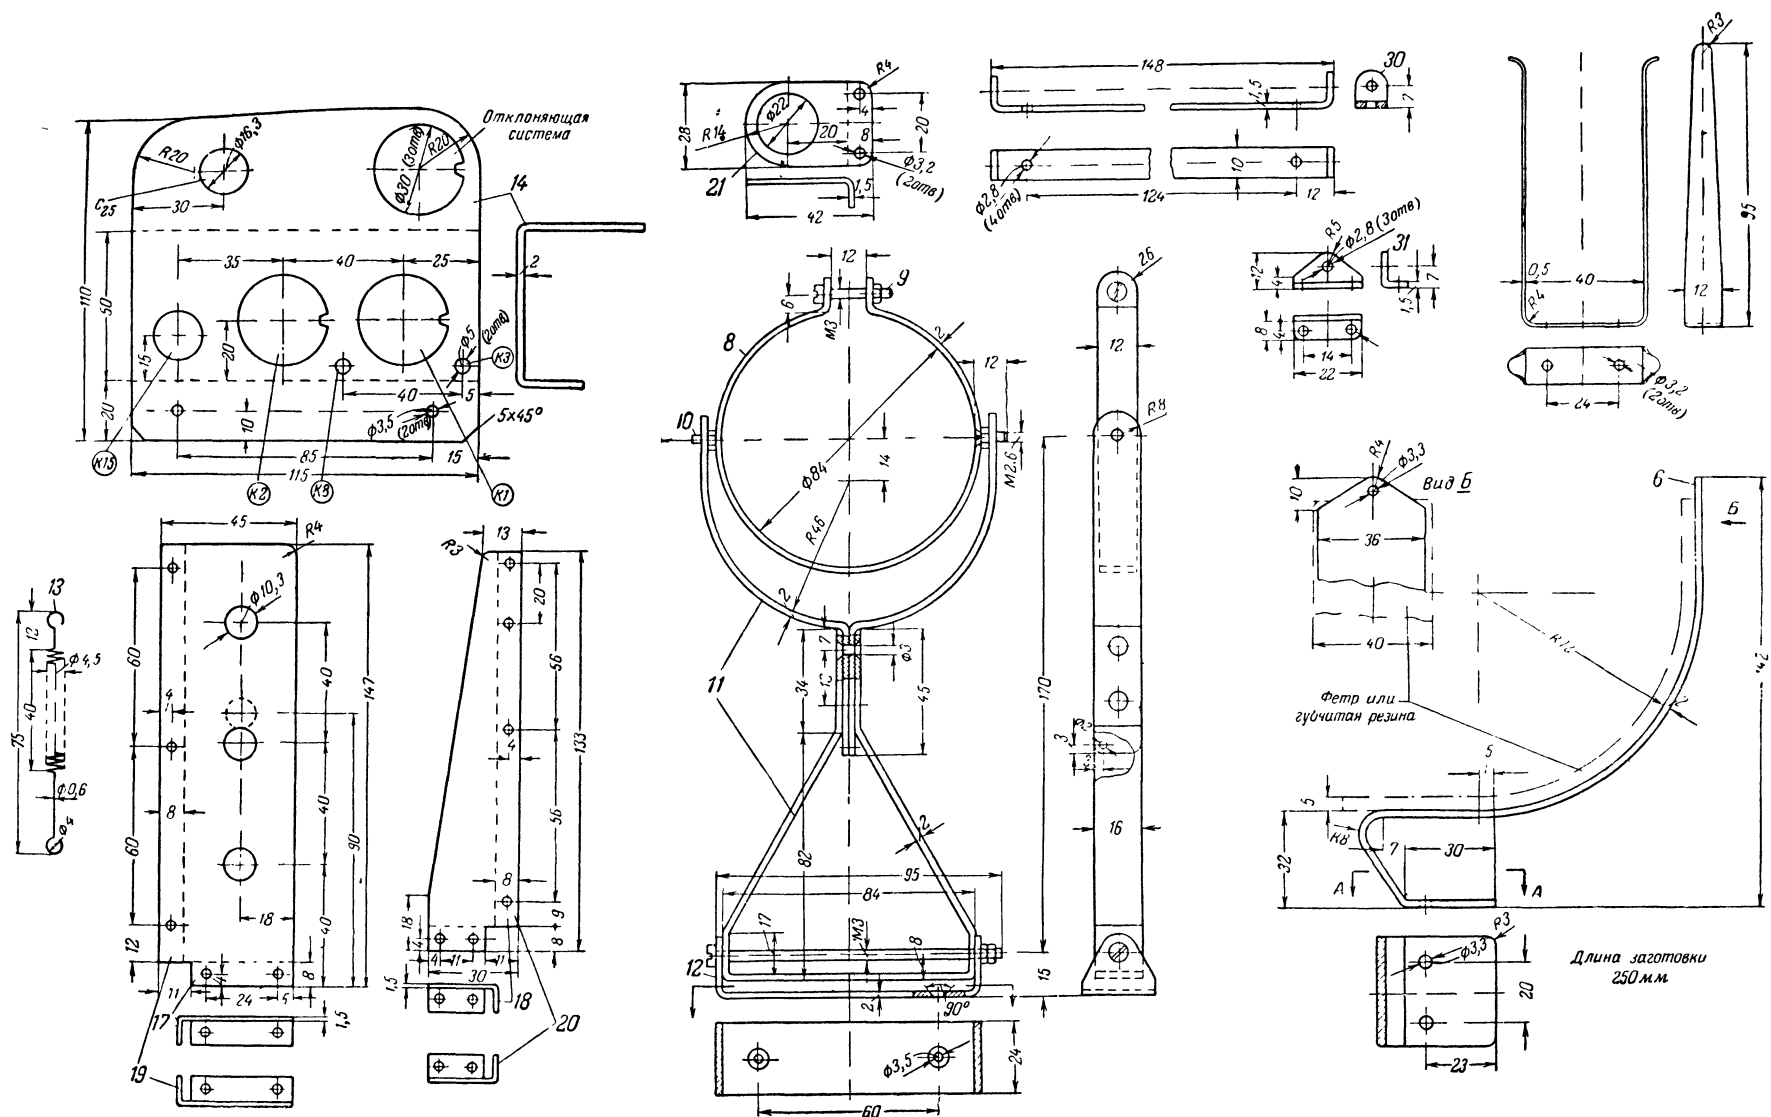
Детали блока разверток (нумерация деталей соответствует рис. 23 и 30).
